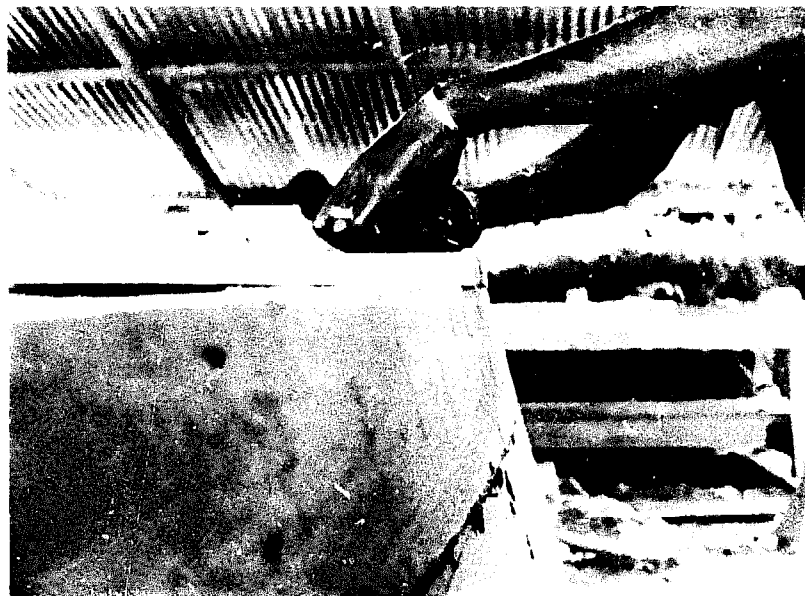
Vous assurer que la planche dépasse d'au moins 2 mm à chaque bout
